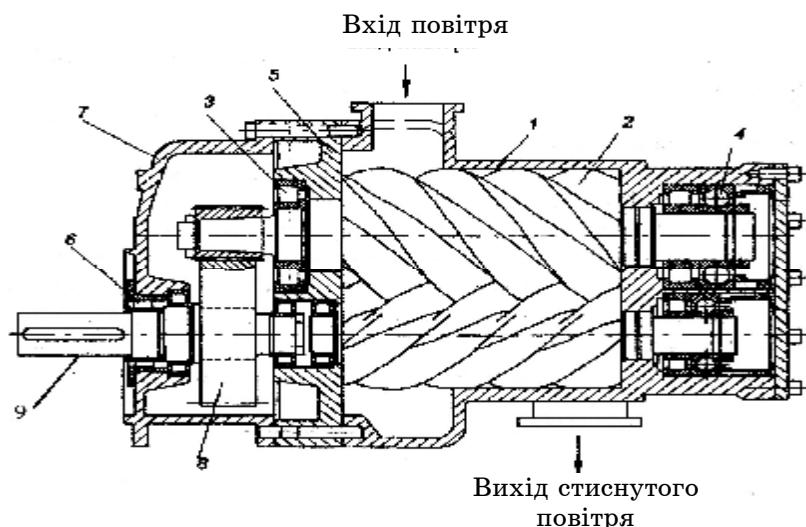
Гвинтовий компресор: 1 - корпус роторної пари; 2 - роторна пара; 3 - роликопідшипник; 4 - шарикопідшипник; 5 - корпус підшипника; 6 - ущільнення; 7 - фланець; 8 - редуктор; 9 – вал привода
